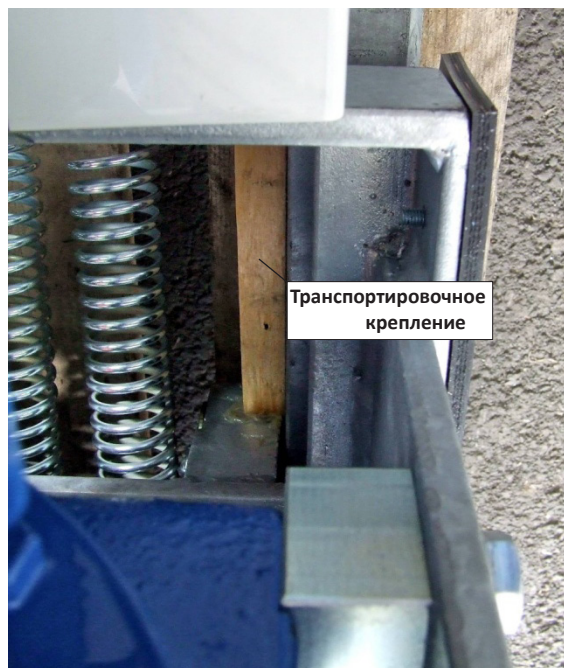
Положение транспортировочного крепления (вид сверху)
